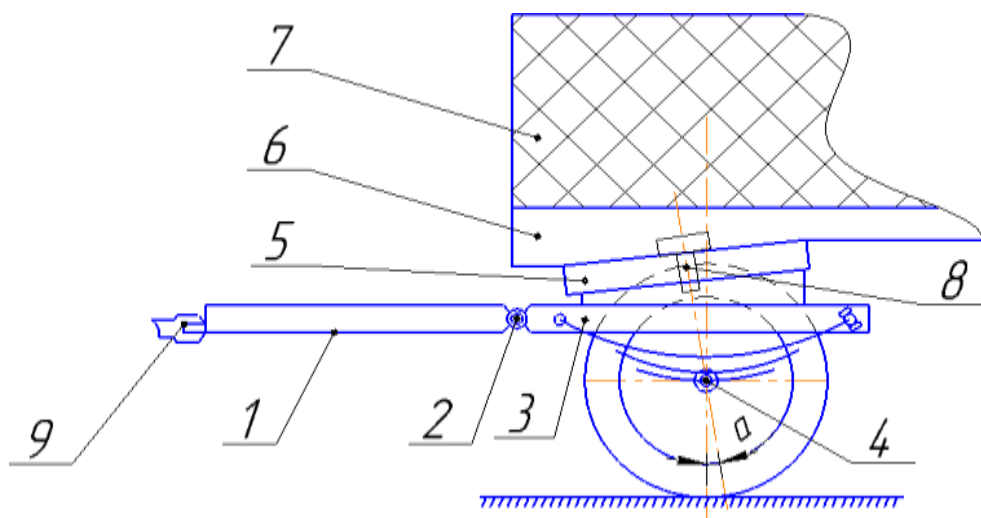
Схема опорно-поворотного пристрою двохвісного причепа
